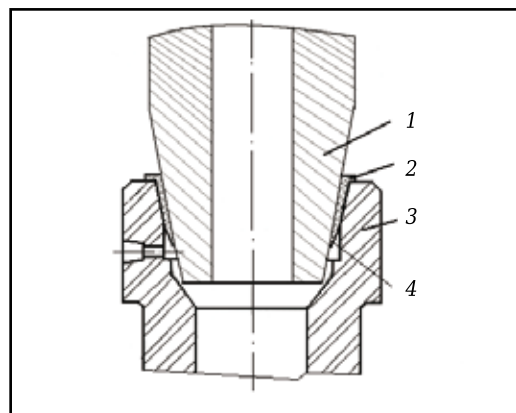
Модернизированное устройство для защиты струи металла при разливке на МНЛЗ: 1 — стакан; 2 — прокладка; 3 — защитная труба; 4 — нижняя торцевая поверхность прокладки
